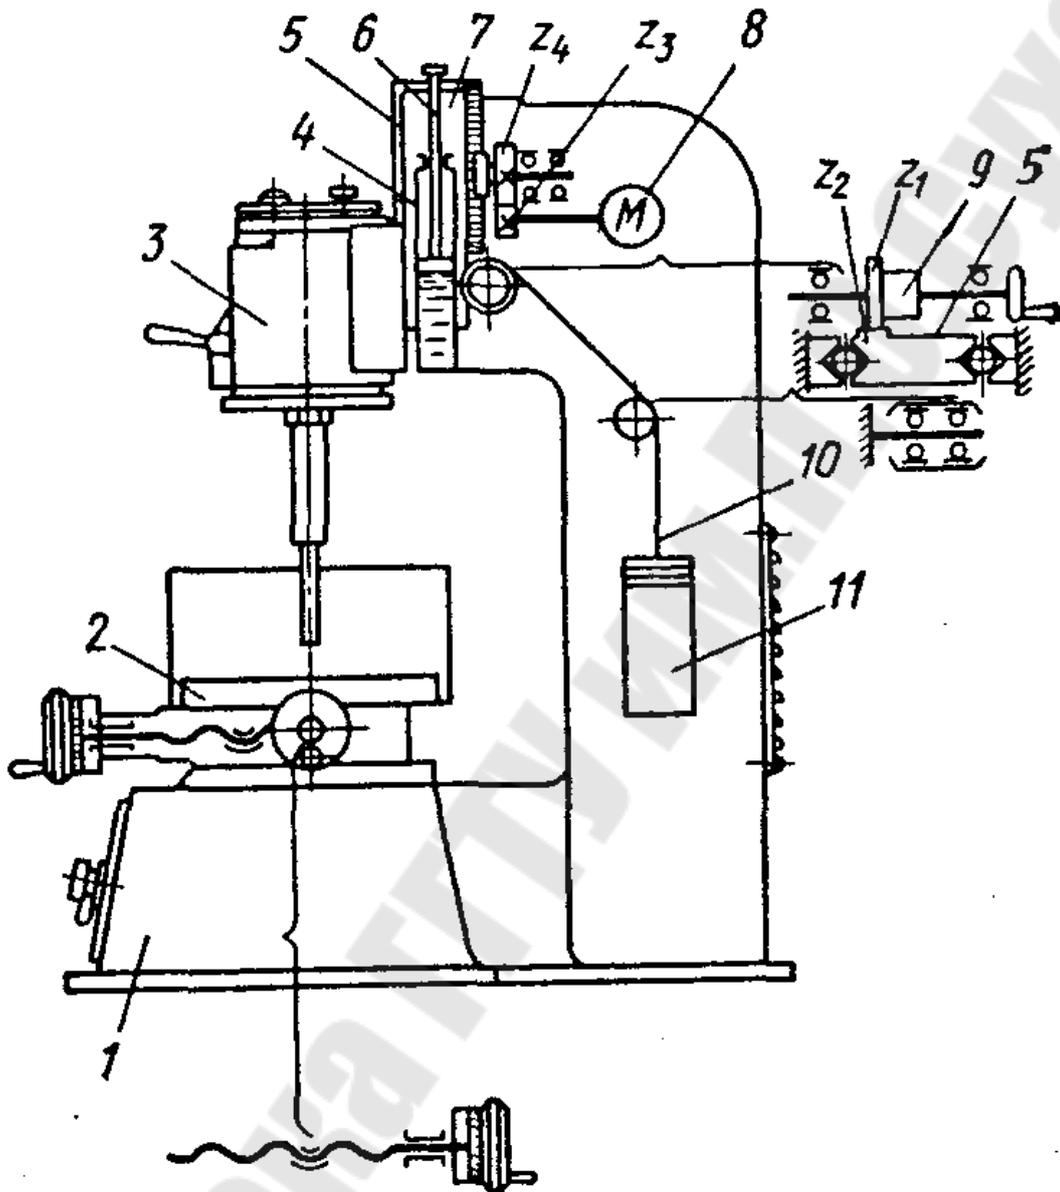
Кинематическая схема универсального ультразвукового прошивочного станка
